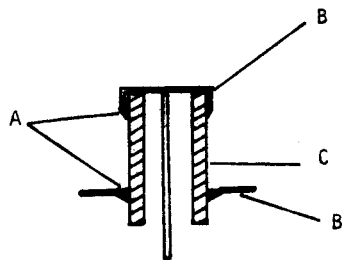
Diseño de un traspasador para alto-vacío. A soldadura. B acero 446. C cerámica  $Al_2O_3$ .
